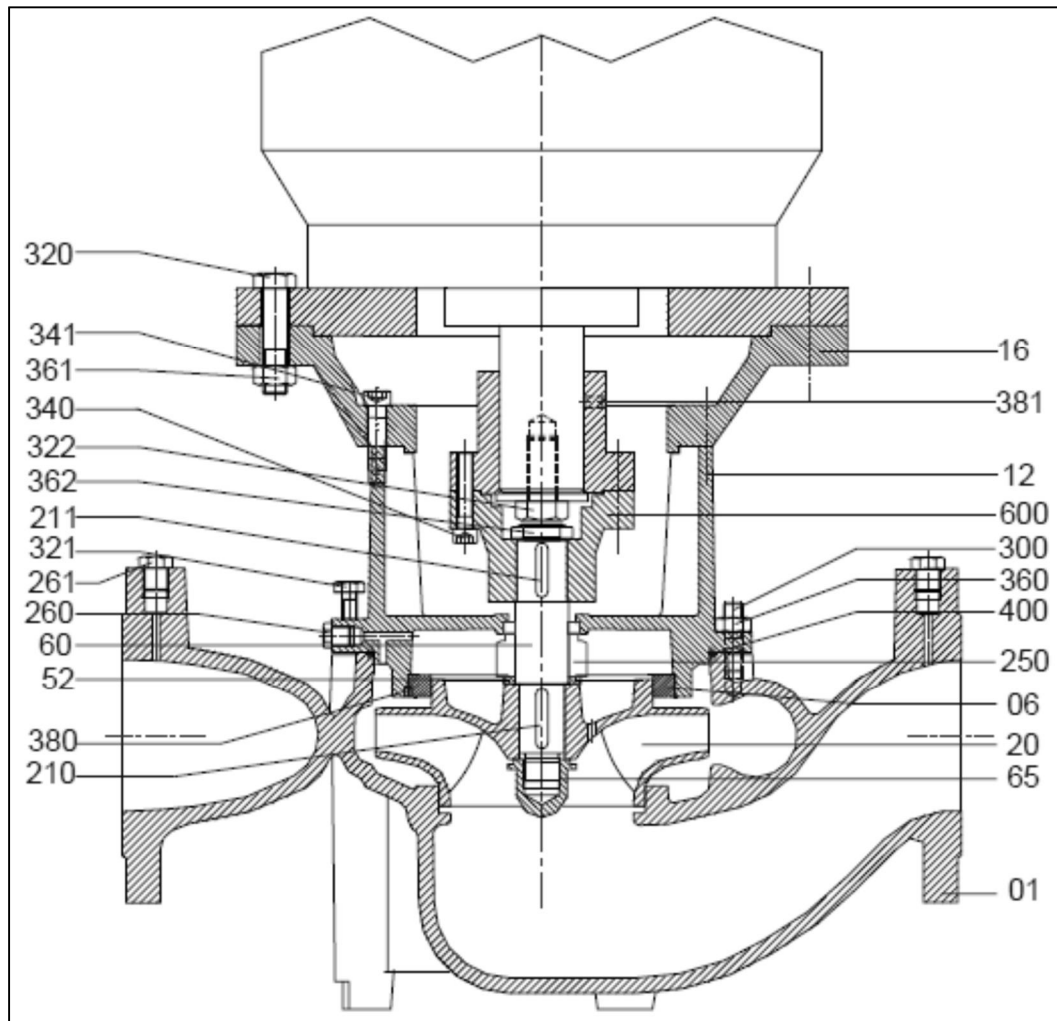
Schnittzeichnung SKI ab 30 kW
